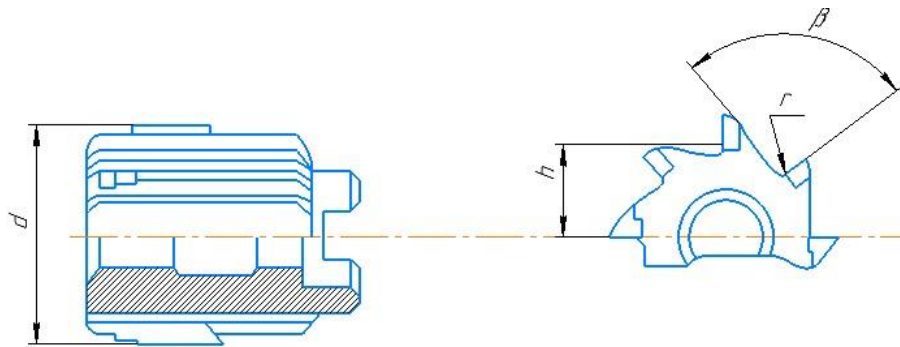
Насадна розвертка з твердосплавними припаяними пластинами
